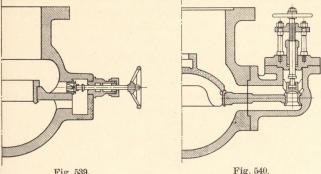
Fig. 539 u. 540. Ventile mit Umführung.
